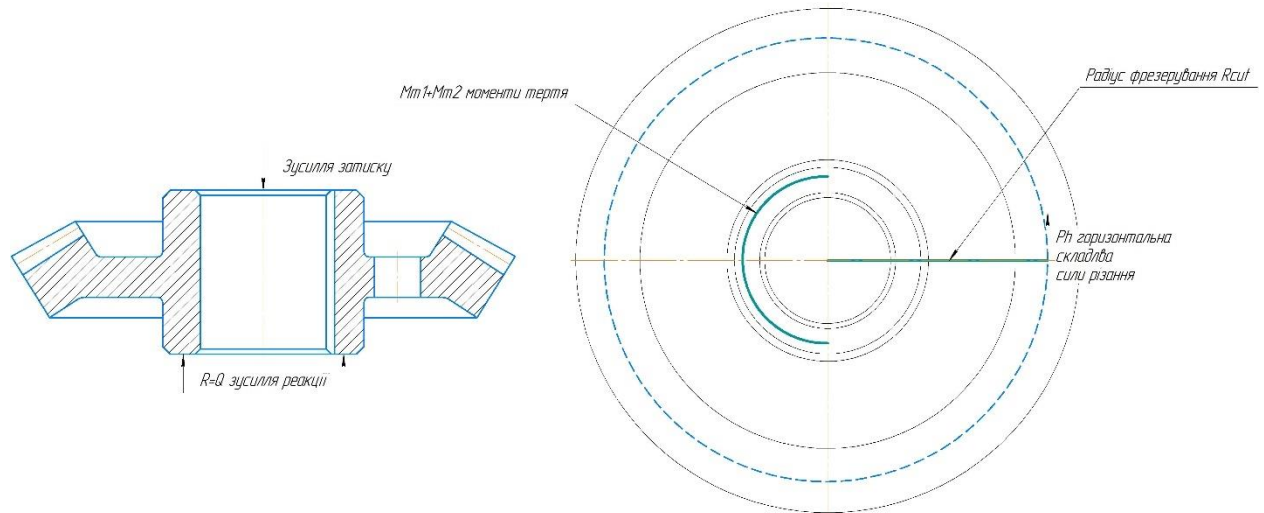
Розрахункова схема для пристосування для зубофрезерування
